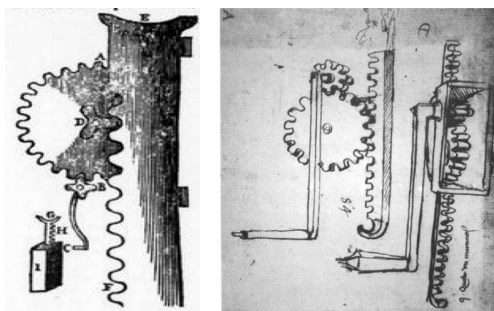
Слева чертеж механизма для преобразования вращательного движения в поступательное, сделанный Галилео Галилеем¹⁹⁹, а справа – Леонардо да Винчи²⁰⁰. Эта машина состоит из кривошипа, понижающей передачи и стержня с зубцами, который движется вверх и вниз
